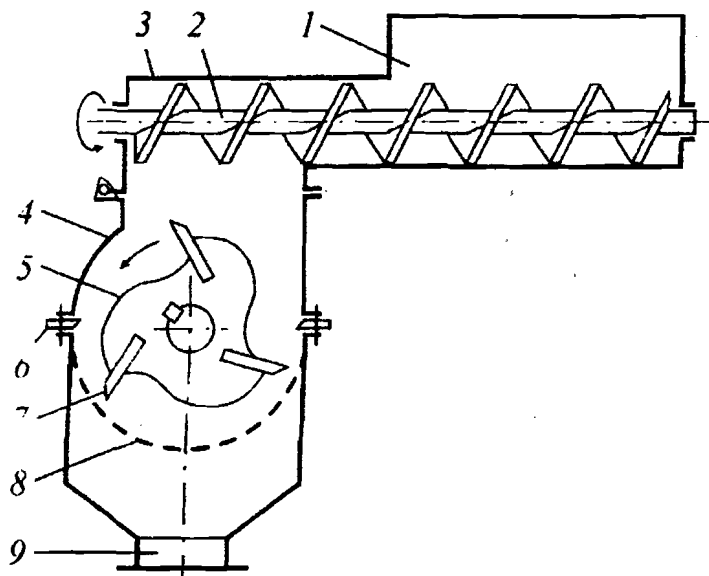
Схема ножевой дробилки с червячным питателем:
